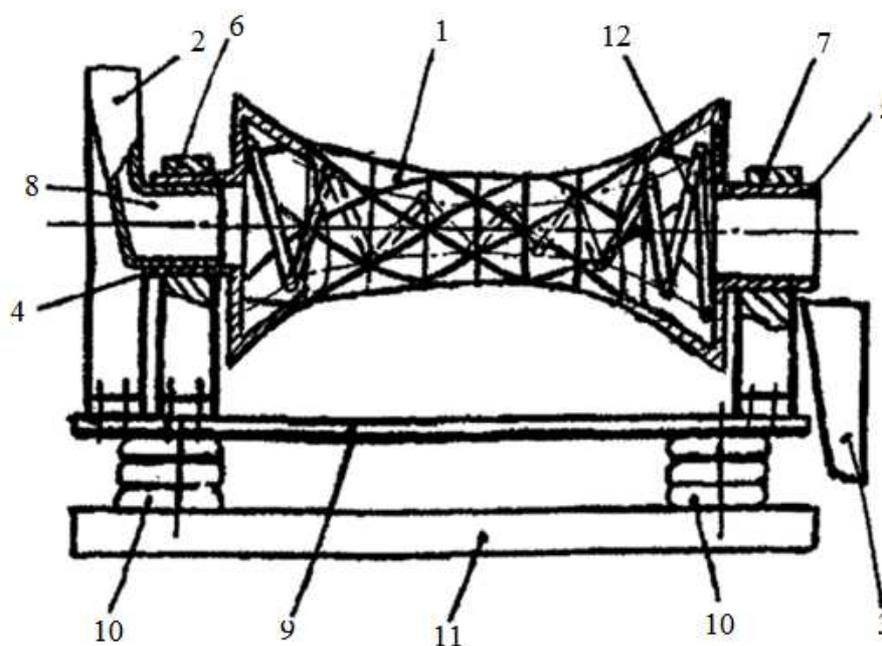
Устройство для приготовления концентрированных кормов (1-винтовой барабан, 2- загрузочное приспособление, 3- разгрузочное приспособление, 4 и 5–втулки, 6 и 7- подшипниковые опоры, 8-носок загрузочного приспособления, 9- рама, 10-четыре пневмобаллона, 11- станина, 12- пружина растяжения)
